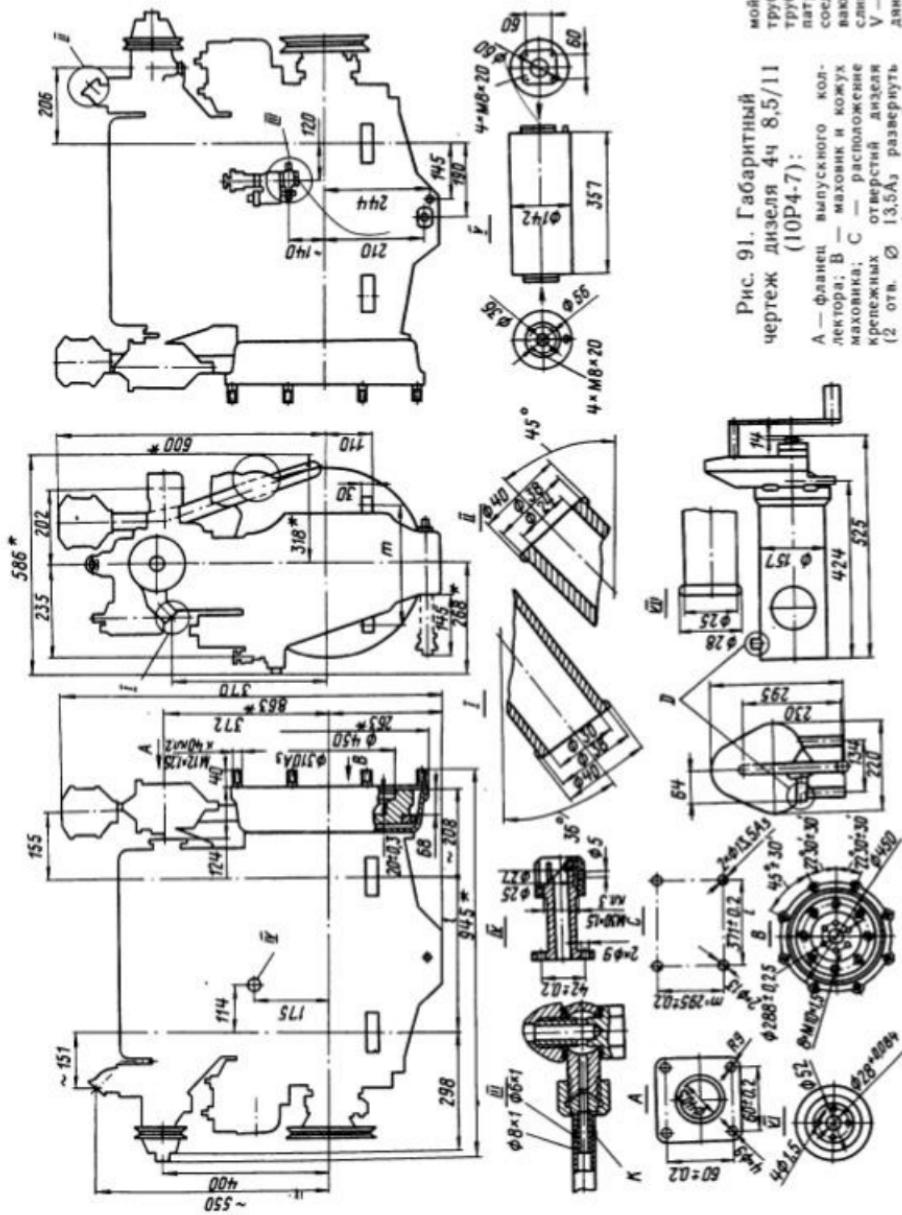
Габаритный чертеж дизеля 4Ч 8,5/11 (10P4-7):
